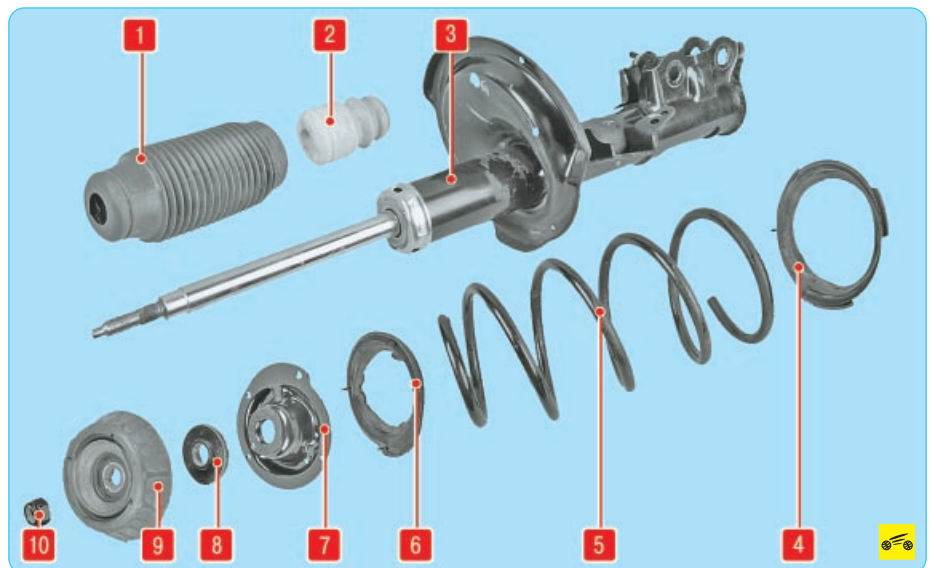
Детали амортизаторной стойки передней подвески: 1 – защитный чехол; 2 – буфер хода сжатия; 3 – амортизатор; 4 – нижняя прокладка пружины; 5 – пружина; 6 – верхняя прокладка пружины; 7 – верхняя опорная чашка; 8 – опорный подшипник; 9 – верхняя опора амортизаторной стойки; 10 – гайка штока амортизатора
